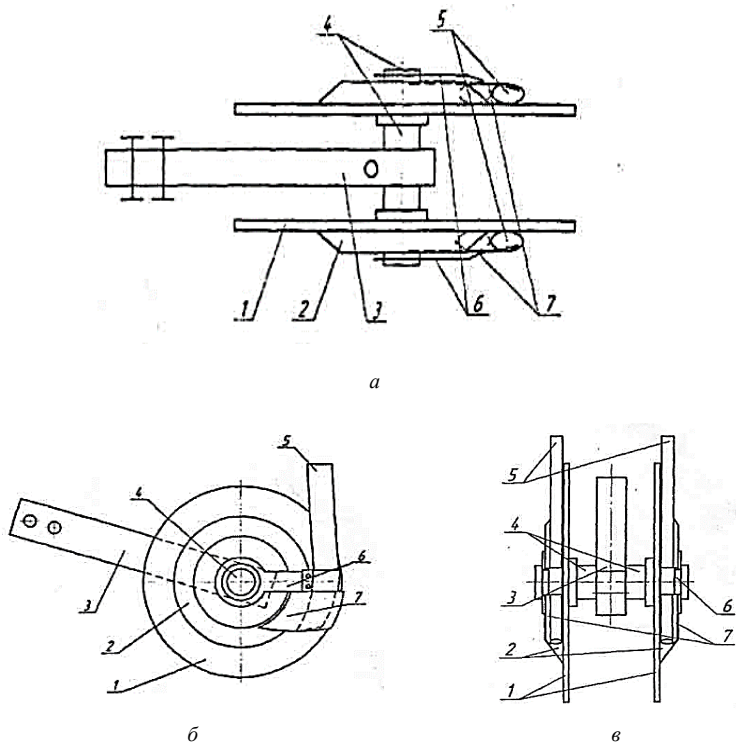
Комбинированный двухдисковый сошник с конусными ребрами и нулевым углом атаки дисков: а – вид сверху; б – вид сбоку; в – вид сзади; 1 – плоские диски; 2 – ребры-бороздкообразователи; 3 – корпус; 4 – ось; 5 – семянаправители; 6 – пластины; 7 – козырьки
